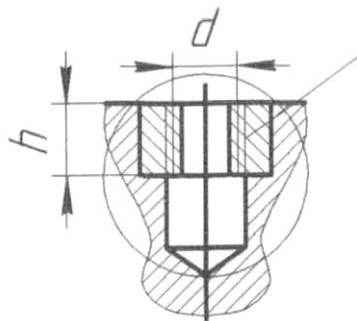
Різьбове з'єднання з різбовою пробкою.
